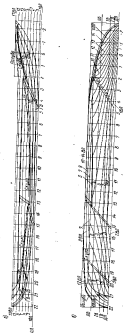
Теоретический чертеж корпуса теплохода «Вихрь»: а — корпус; б — бак — топливника.
